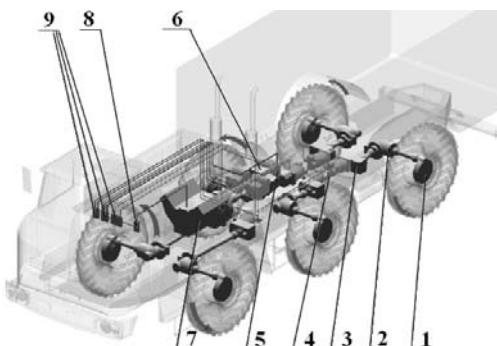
ГОМТ і автоматична система керування «Гидроход-49061»: 1 – колісний редуктор; 2 – бортовий редуктор; 3 – погоджувальний редуктор гідромотора; 4 – гідромотор; 5 – насос; 6 – редуктор насосної станції; 7 – двигун внутрішнього згоряння; 8 – мікропроцесор керування двигуна; 9 – мікропроцесори керування гідронасосами і гідромоторами
